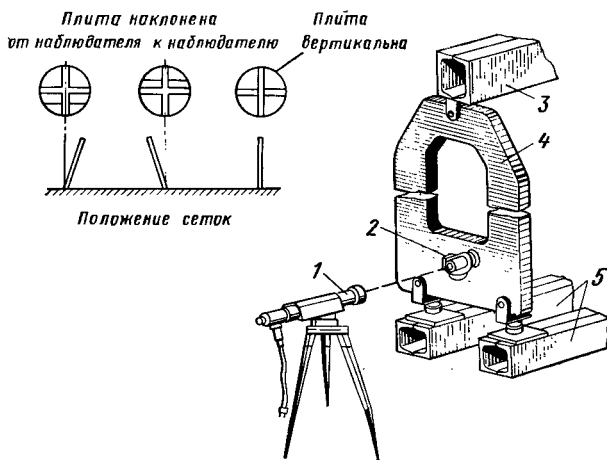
Схема проверки автоколлиматором вертикальности плиты сборочного приспособления:
